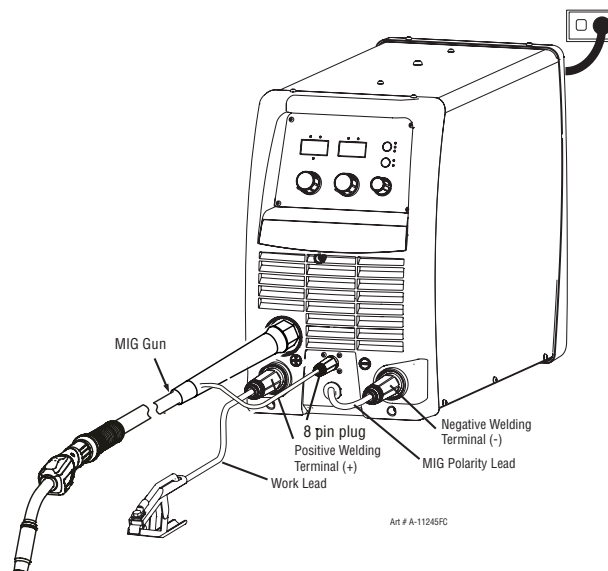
Configuration pour soudage MIG (FCAW) avec fil-électrode fourré (sans protection gazeuse)
